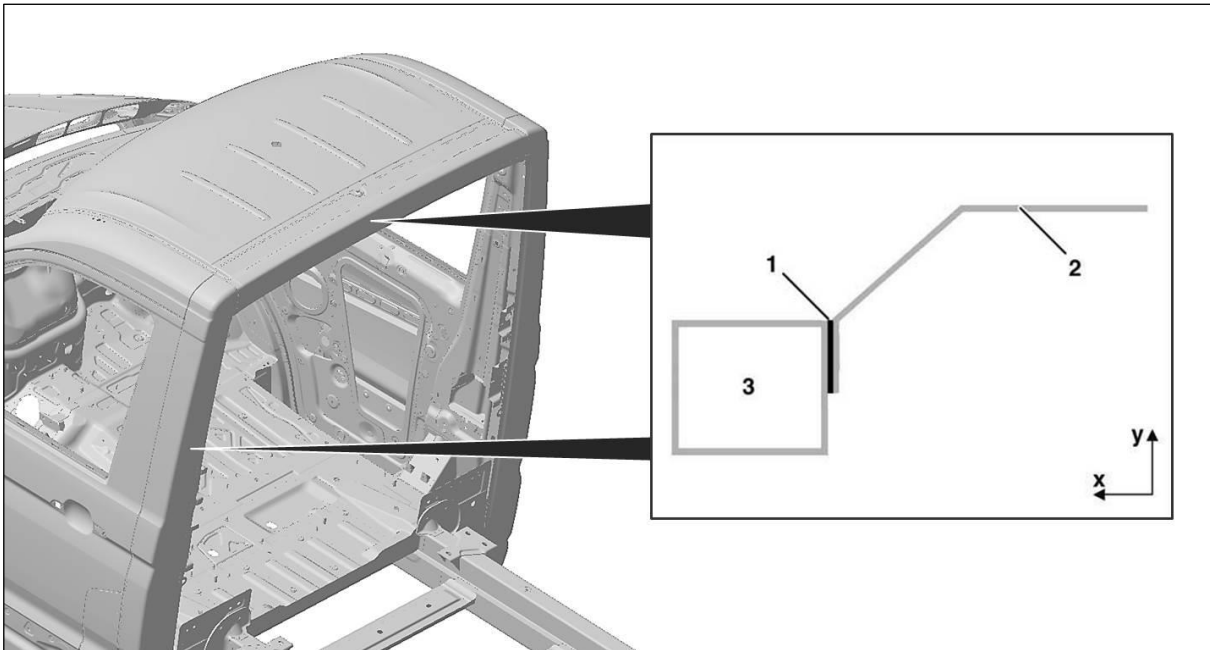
fissaggio sovrastruttura tramite lamiera verticale su montante B e telaio del tetto (rappresentazione schematica!)
